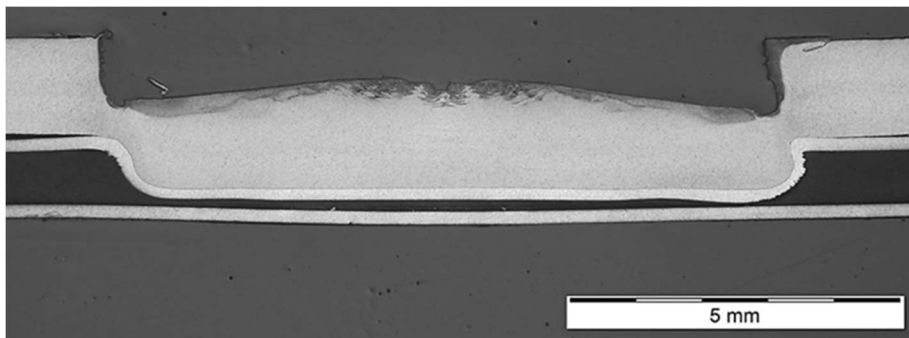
Werkingsprincipe van friction stir spot welding
